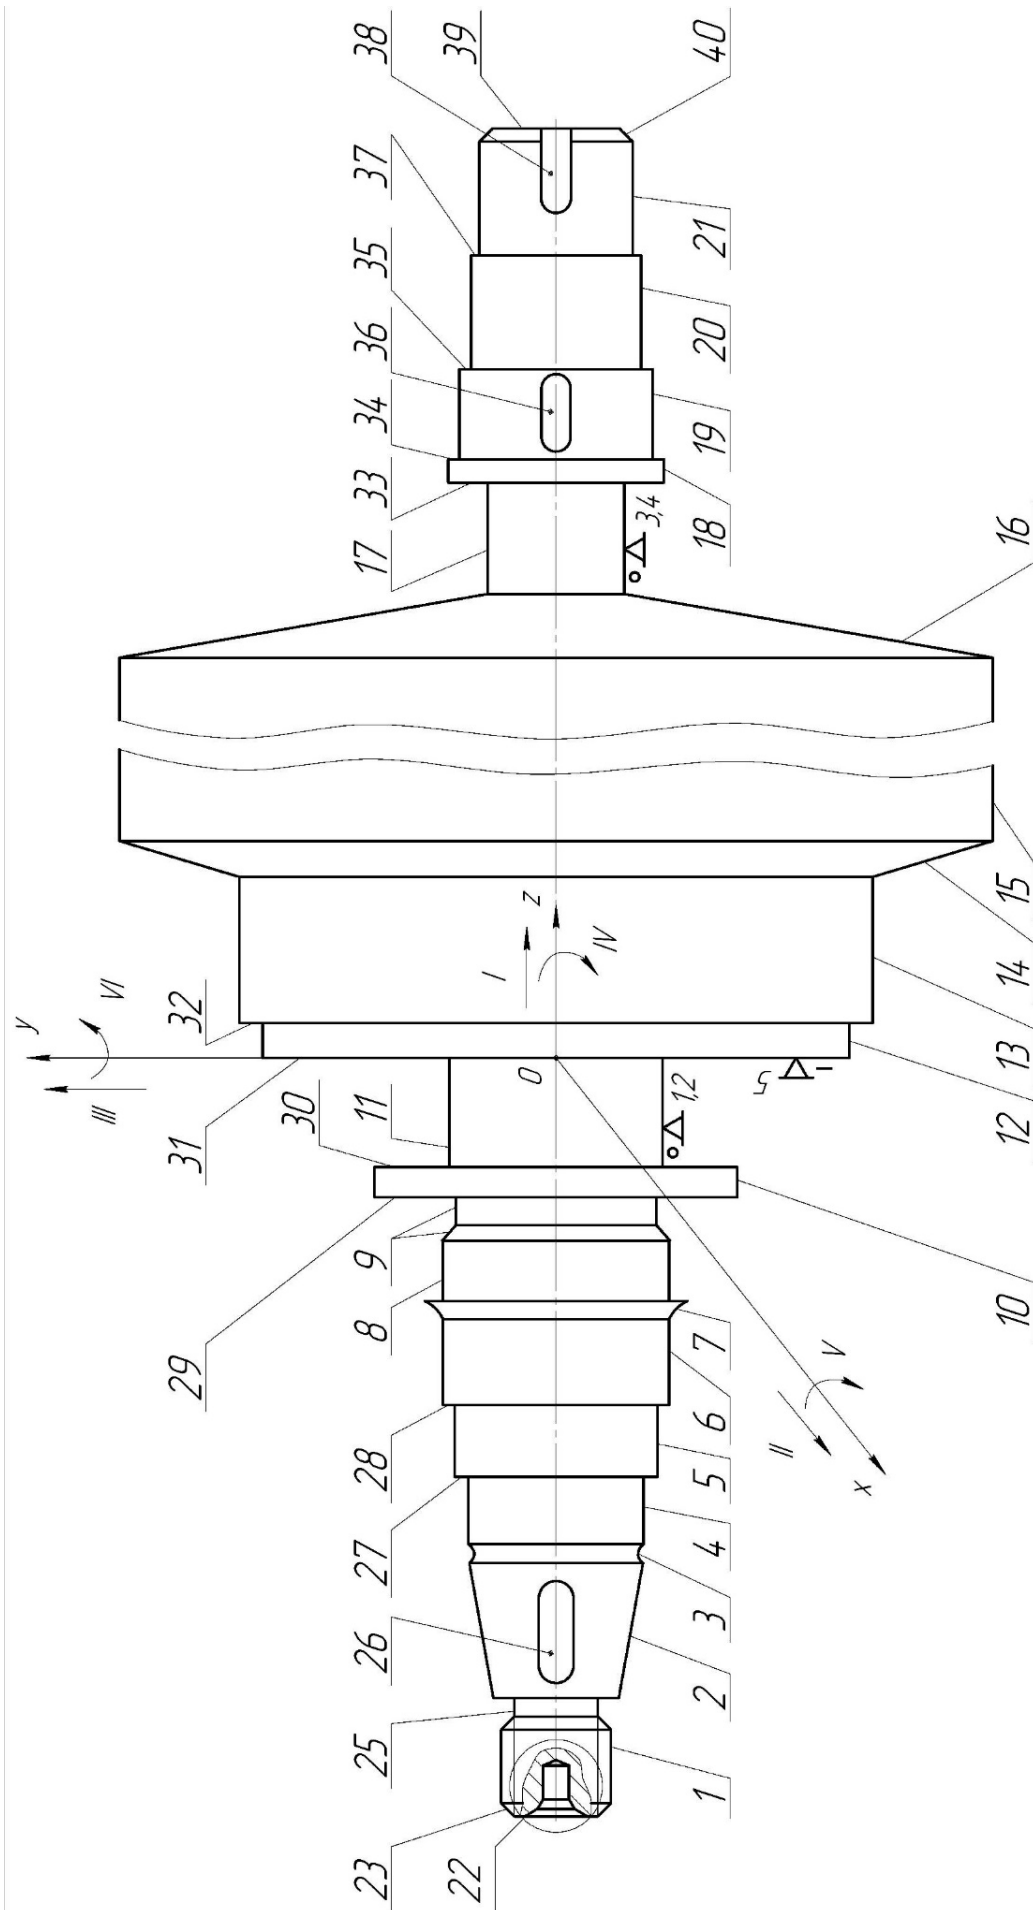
Креслення вала 298Н-25-01 із нумерованими поверхнями
